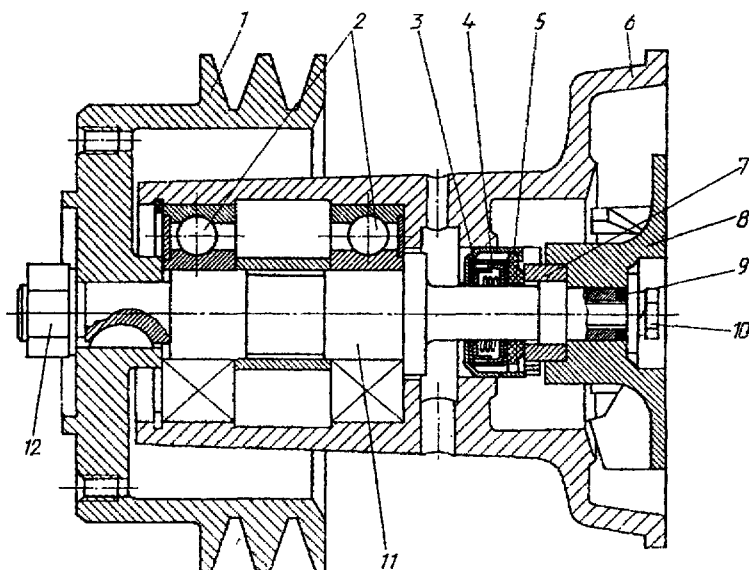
Насос системы охлаждения (продольный разрез, Д-245): 1 – шкив; 2 – подшипники полузакрытого типа; 3 – манжета; 4 – пружина; 5 – шайба; 6 – корпус; 7 – втулка; 8 – крыльчатка; 9 – резиновое кольцо; 10 – болт; 11 – валик насоса; 12 – гайка
